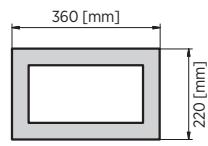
Tipo AP-4, dimensioni 360x220 [mm].
